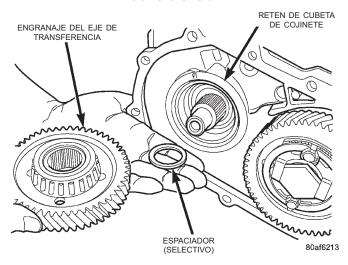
Desmontaje del engranaje del eje de transferencia y espaciador (selectivo)
